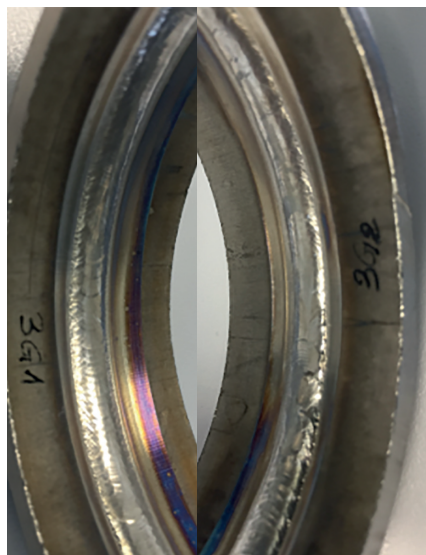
Сварной шов, на подъем – слева, на спуск – справа
